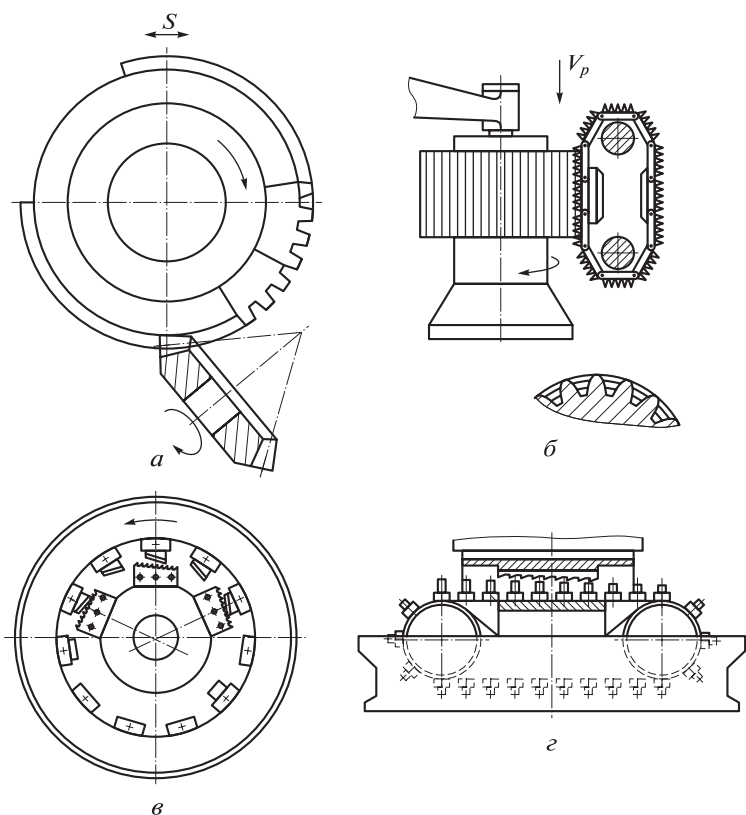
Принцип работы протяжных станков непрерывного действия: *а* — работающих дисковой протяжкой; *б* — работающих гибкой протяжкой; *в* — с неподвижным комплектом протяжек и движущимися по круговой траектории обрабатываемыми деталями; *г* — с неподвижным комплектом протяжек и движущимися прямолинейно заготовками
